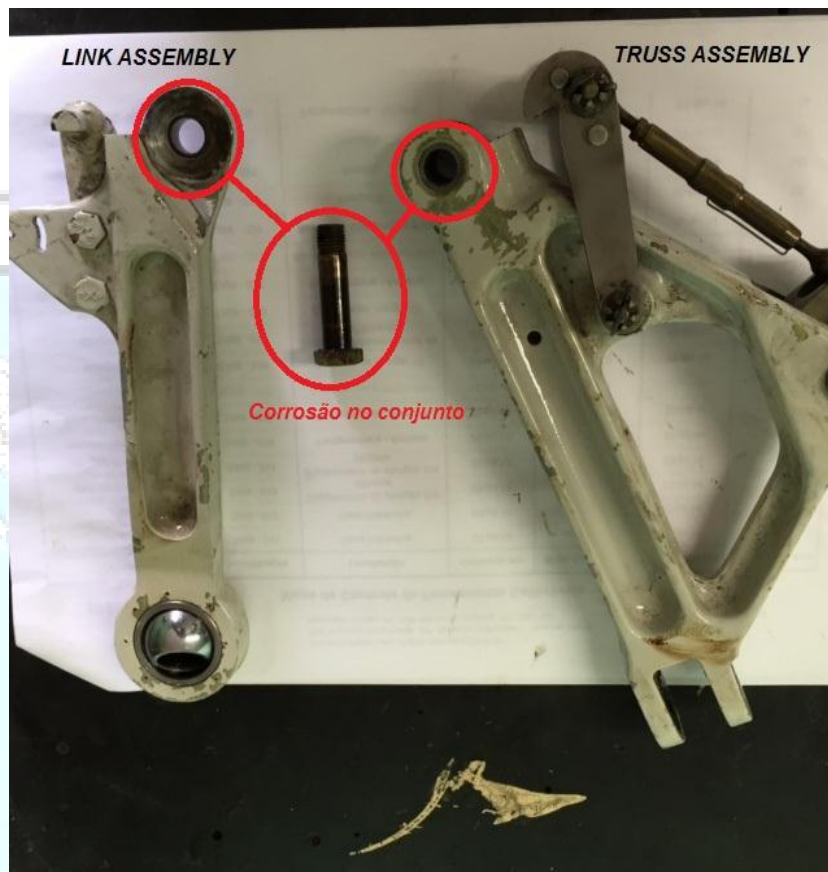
Corrosão no conjunto do braço de retração do trem de pouso principal esquerdo, PN 39470-02 e PN 39472-02.
